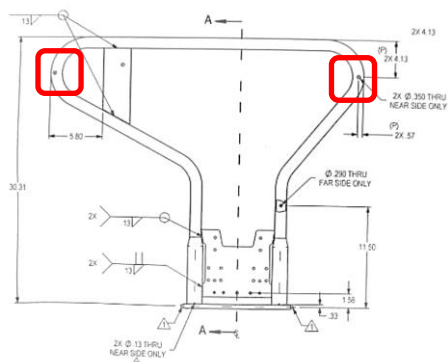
Handrail, Weld Assembly, Folding, Lh
